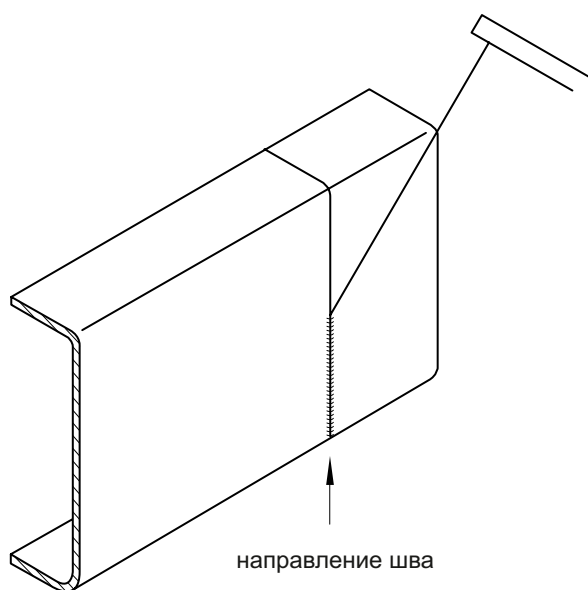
Вертикальный сварной шов на раме TDB-090
